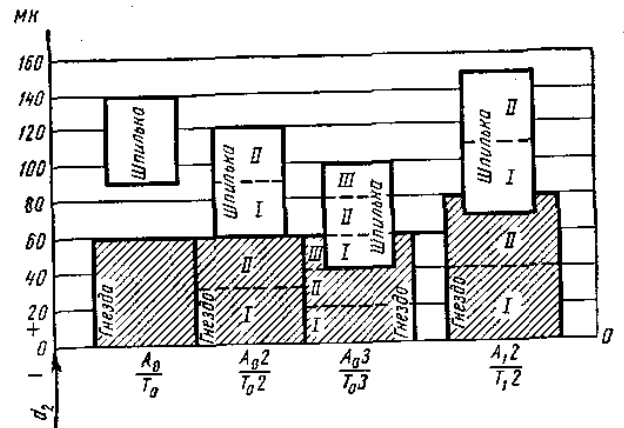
Схема расположения полей допусков среднего диаметра резьбы с натягами (для резьбы М14×1,5)
